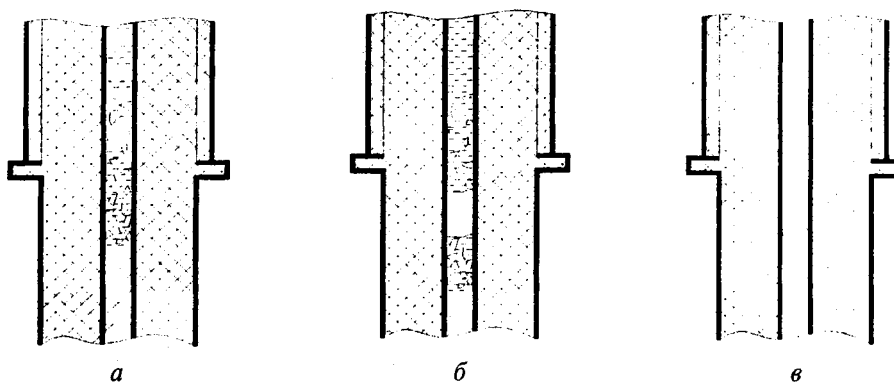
Схема формирования отливки во втулке кристаллизатора
